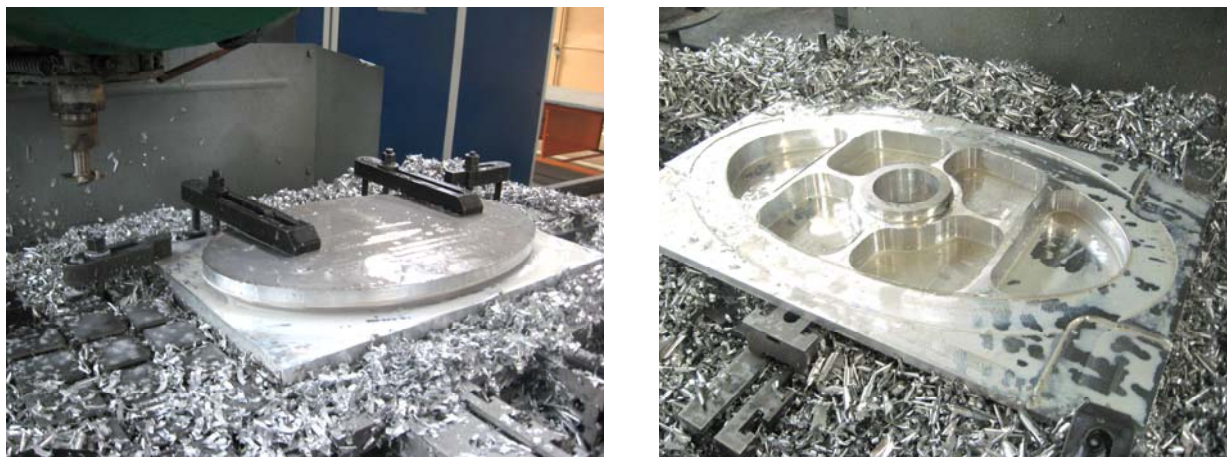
Процесс изготовления крышки люка-лаза (148.00.1080.054.000) на модернизированном станке ФП-7СМН5
